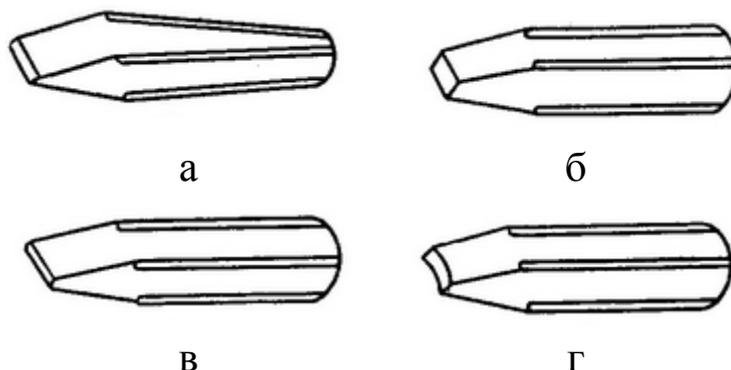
Типы чеканов: а - шовный чекан; б – подбойник; в – кругляк; г - заклепочный чекан
